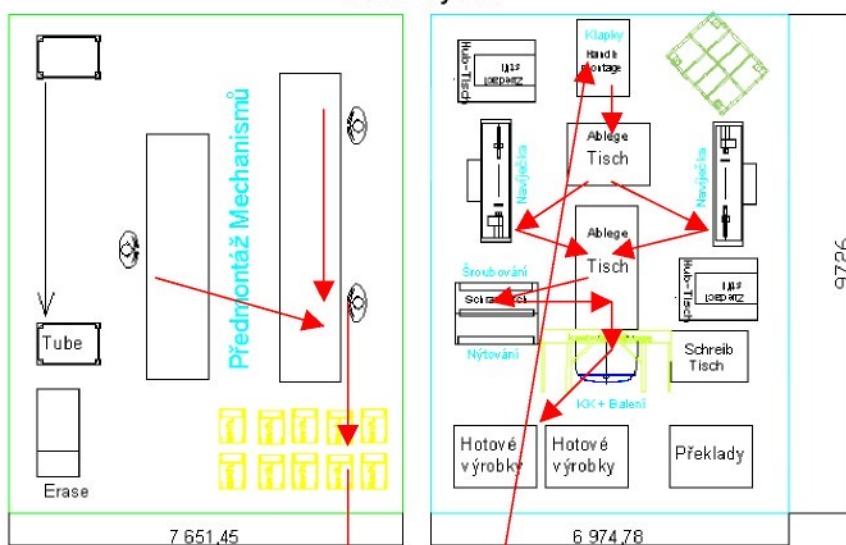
Layout celé výroby krytů zavazadlového prostoru (LC) - souč. stav
